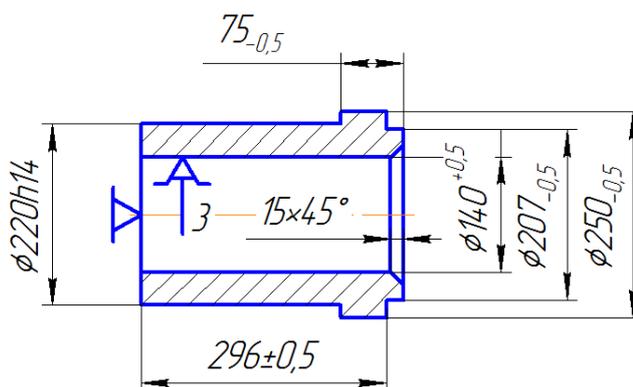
Эскиз базирования заготовки на 010 токарной операции.
